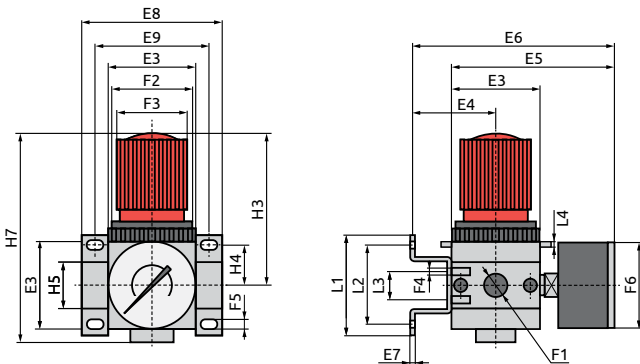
Габаритные размеры блоков подготовки сжатого воздуха ATU-R
